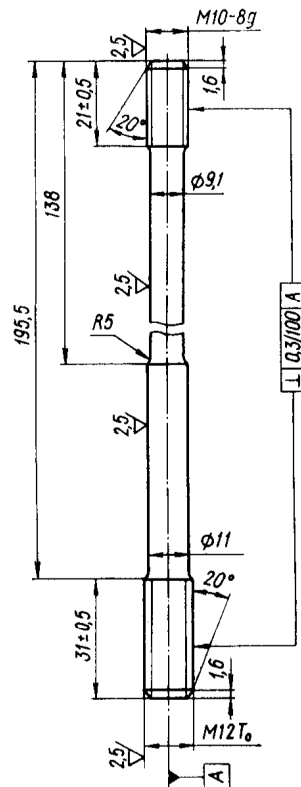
Шпилька крепления головок цилиндров (ремонтная)
